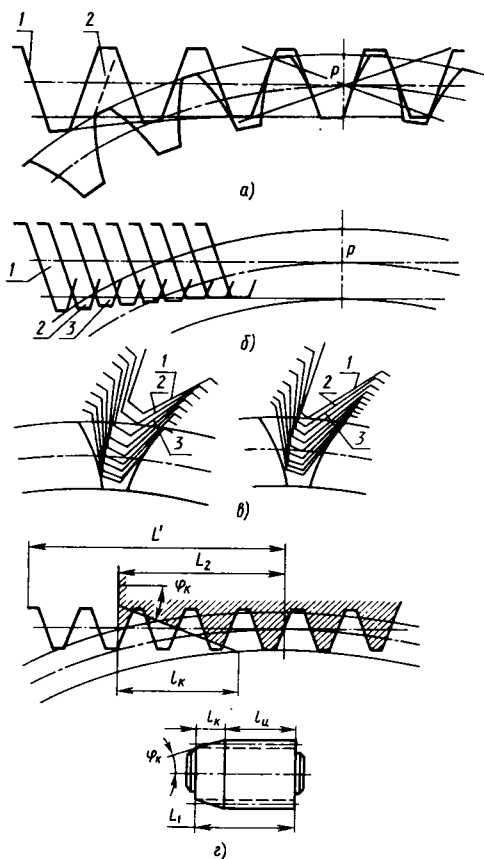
Червячные фрезы с измененной схемой резания черновых зубьев
